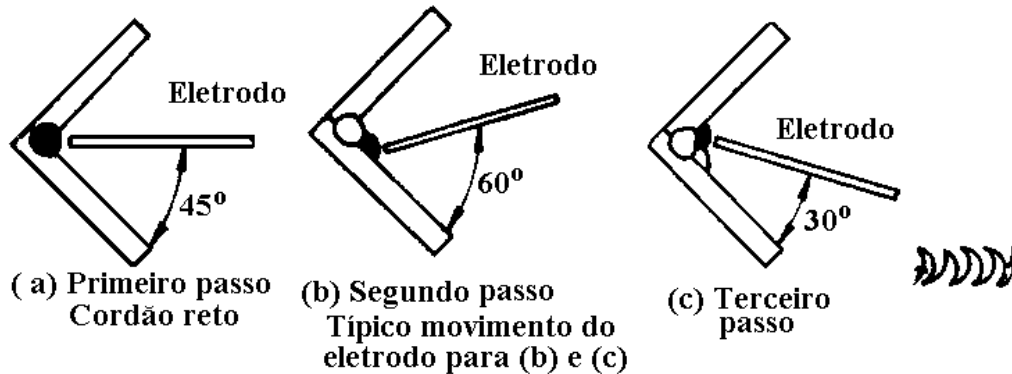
Inclinações de eletrodo na soldagem horizontal.
